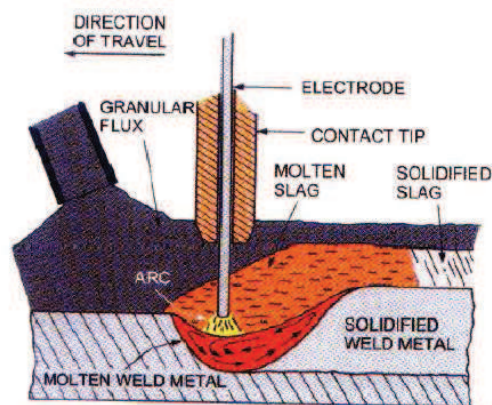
Proceso de soldadura por arco sumergido
